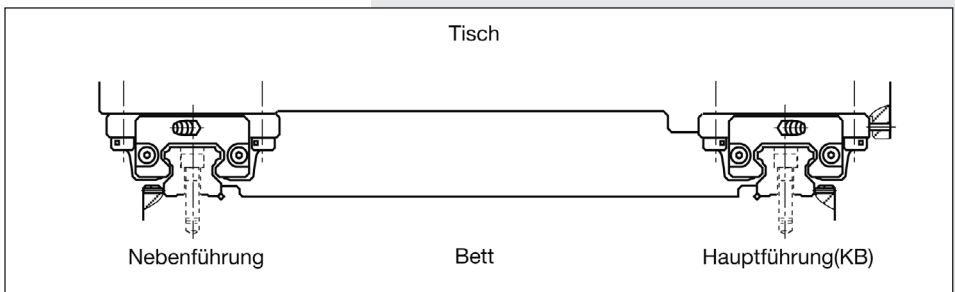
Montage von THK-Linearführungen ohne Andruckschrauben an den Führungsschienen
